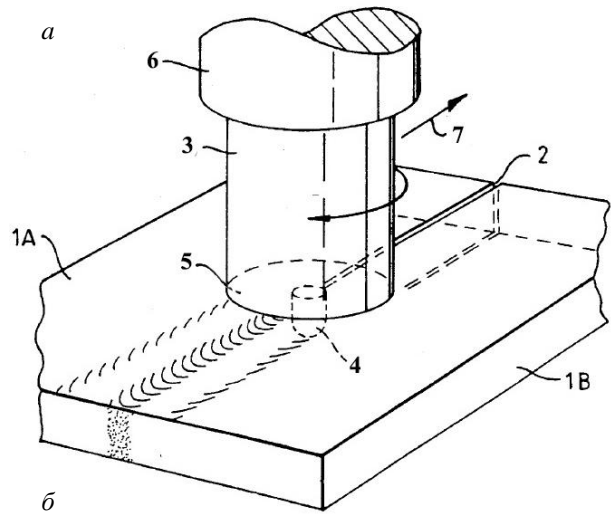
Процес ЗТП двох заготовок (а) та робочий інструмент (б):
